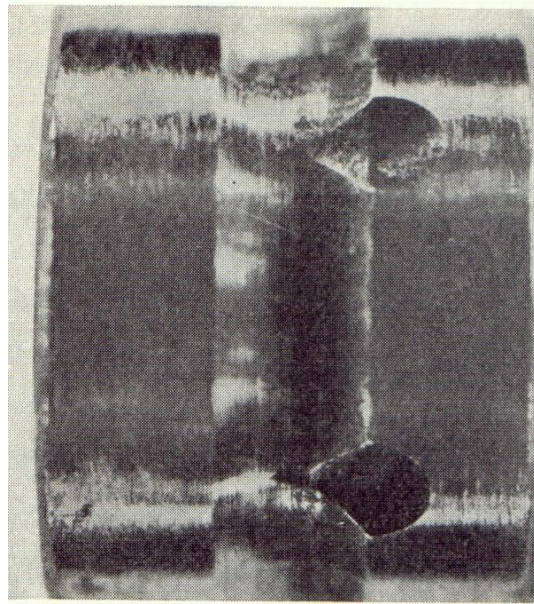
corrosión por vibración axial en la pista interna de un rodamiento de bolas [2].
